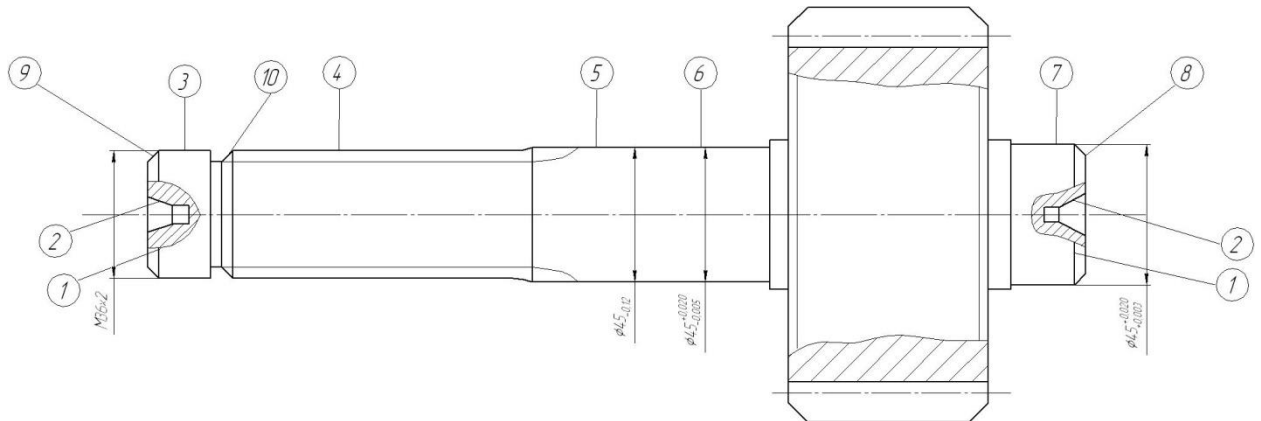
Робочий ескіз вал - шестерні 562-3-354а.
